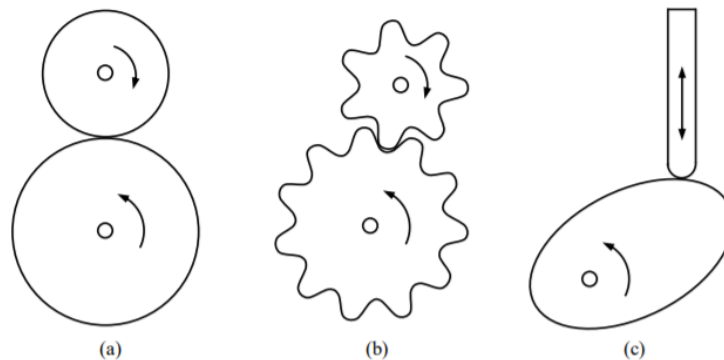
Sistemas de transmissão por contacto directo: (a) Rodas de atrito; (b) Engrenagens; (c) Mecanismo came-seguidor. [20]
